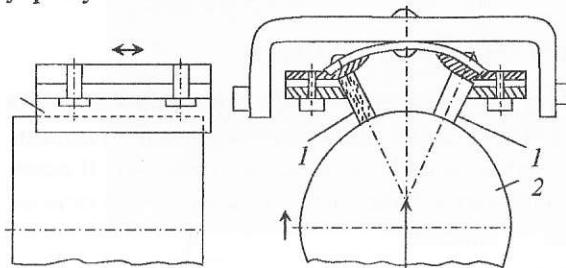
Схема суперфінішування поверхні деталі типу «вал»
